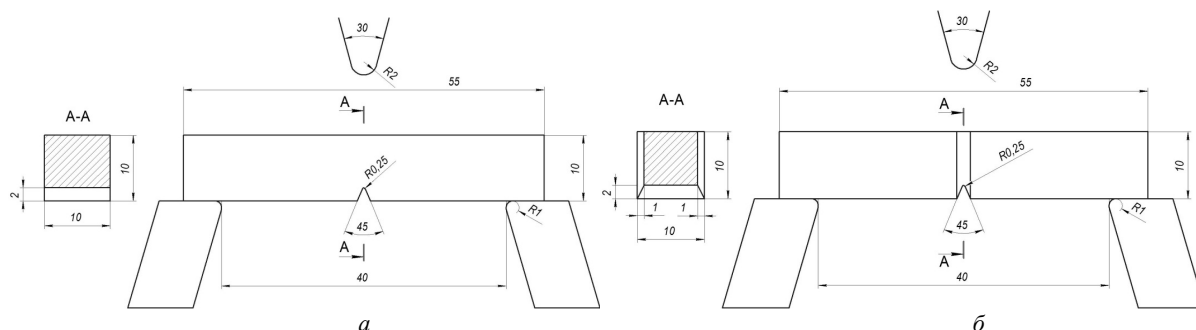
Геометрические размеры стандартного образца Шарпи а) и образца с боковыми выточками б)
